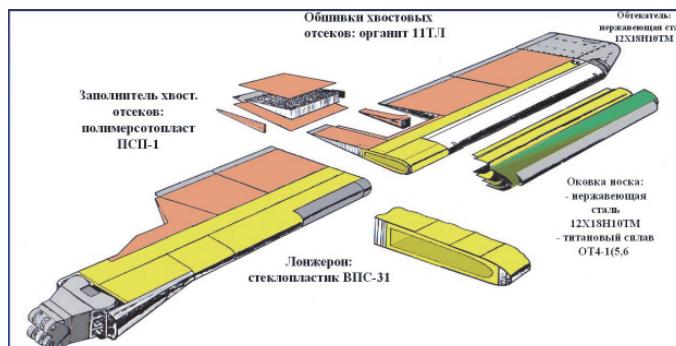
Конструкция лопасти несущего винта для вертолетов Ми-28Н
